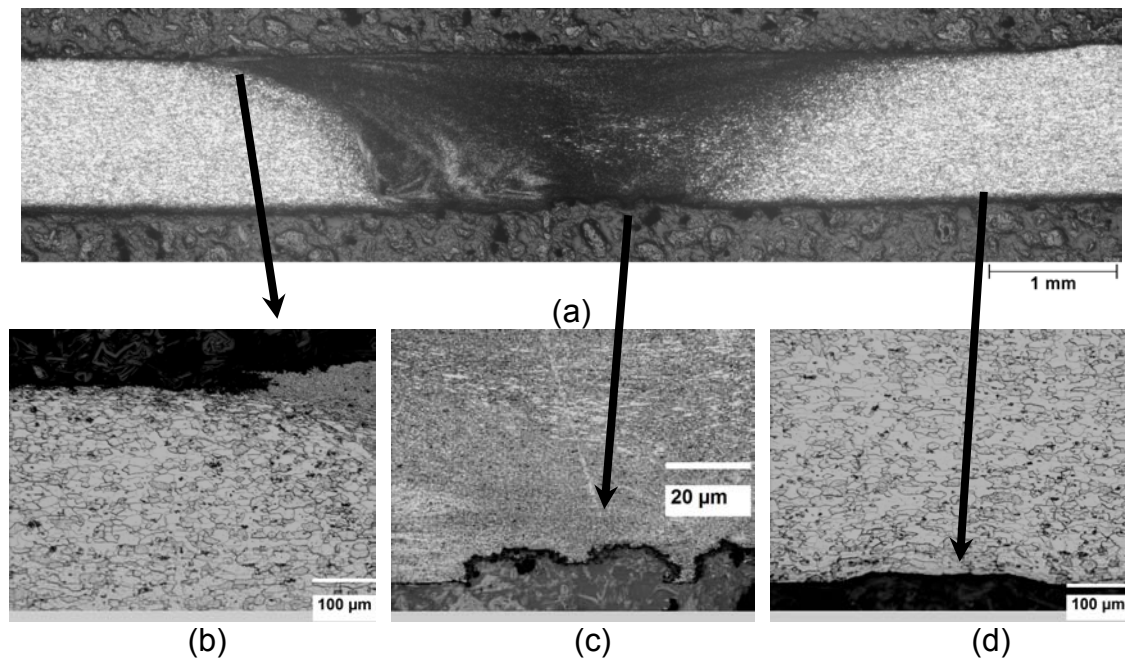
Junta soldada por FSW da liga 2024-T351 após ensaio de corrosão intergranular; (a) seção transversal da junta soldada, (b) corrosão na interface ZTMA e ZTA (c) raiz da junta na região da lente de soldagem, com ataques intensos por pites e (d) ataque de corrosão por esfoliação na região do metal base.
